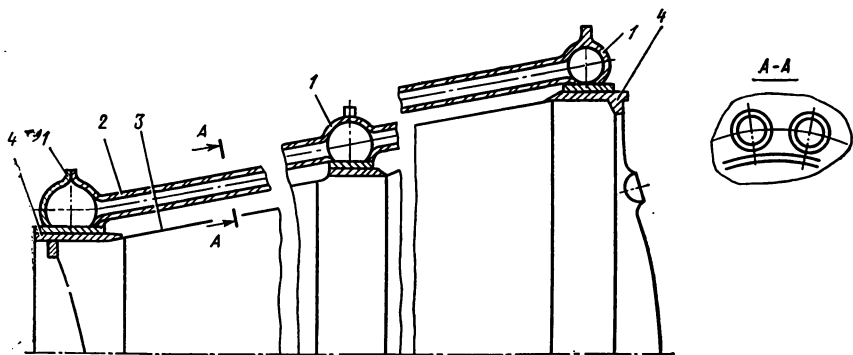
Конический гибкий неразвертывающийся излучатель
